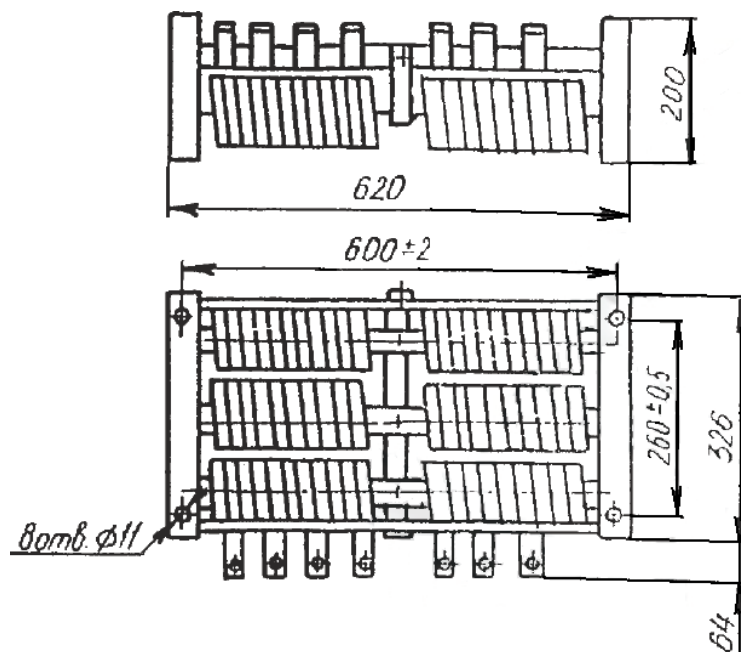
Габаритные и установочные размеры блоков и схема размещения резисторов в блоке.
